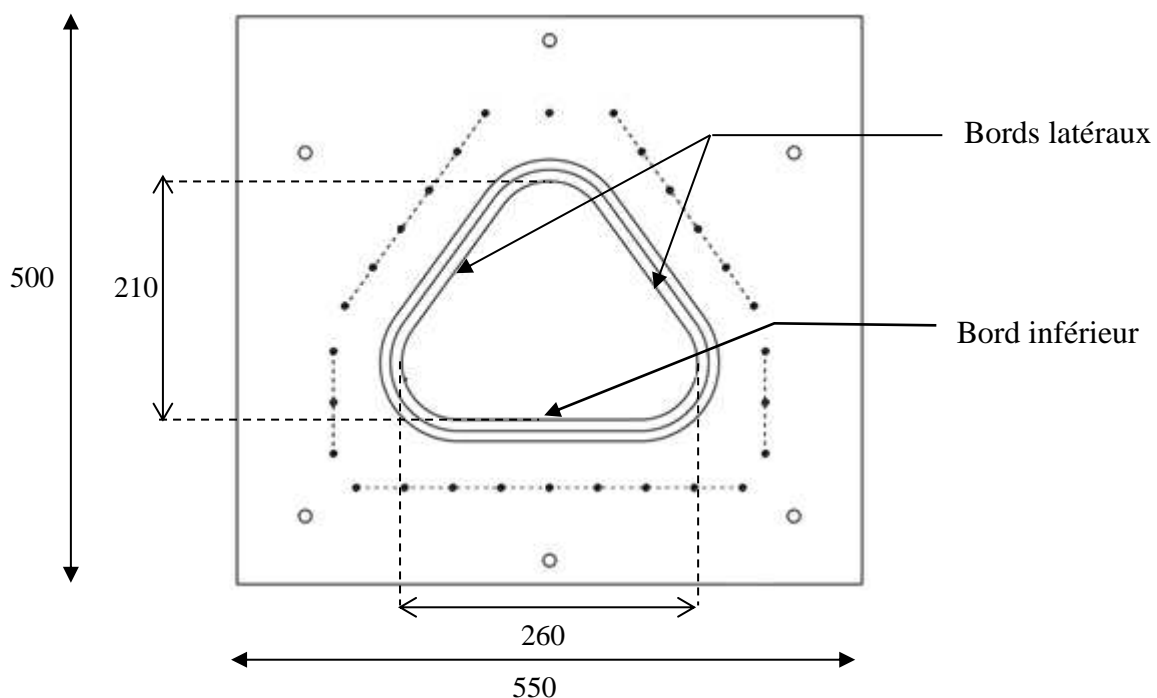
Dimensions de la plaque en aluminium et du trou central. Les dimensions sont en mm.
